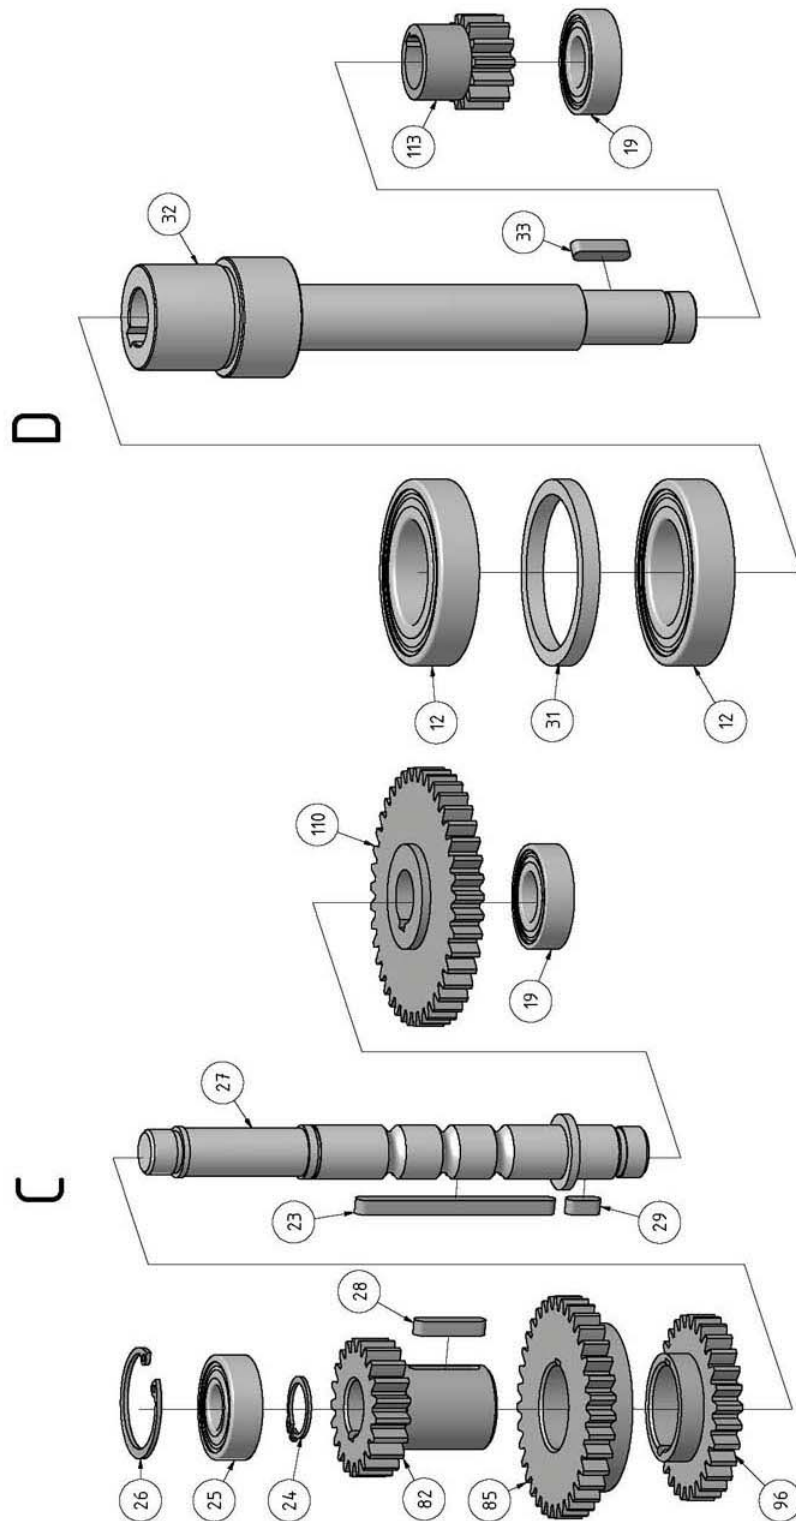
Fräskopf 3 von 6 - Milling head 3 von 6
